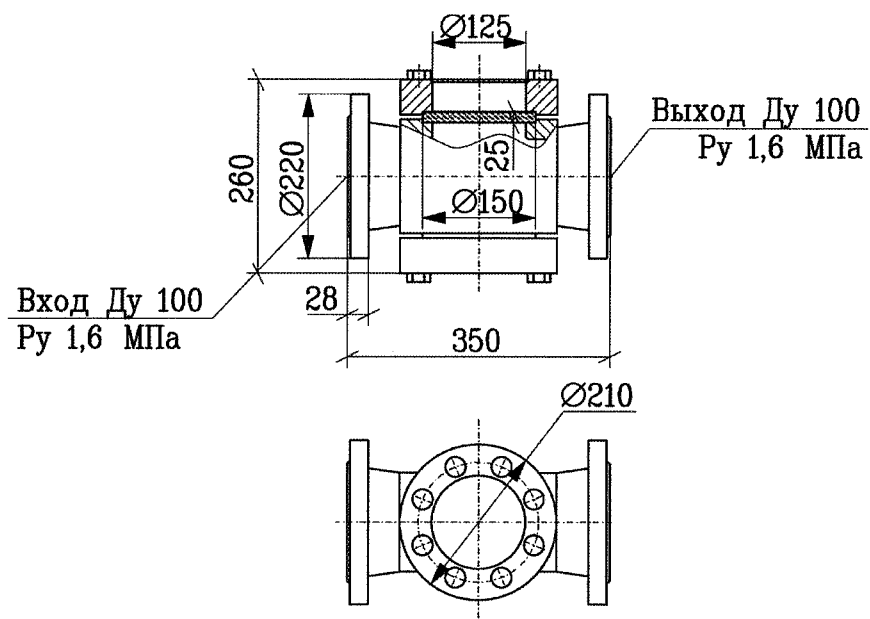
Габаритный чертеж фонаря смотрового LDP42AX001
